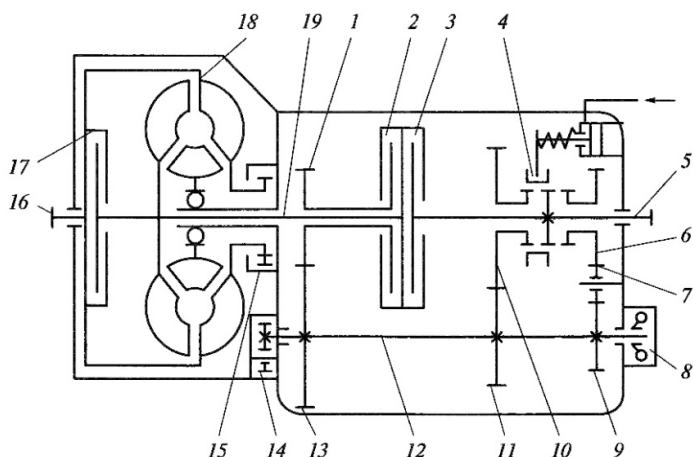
Схема гидромеханической двухступенчатой коробки передач
